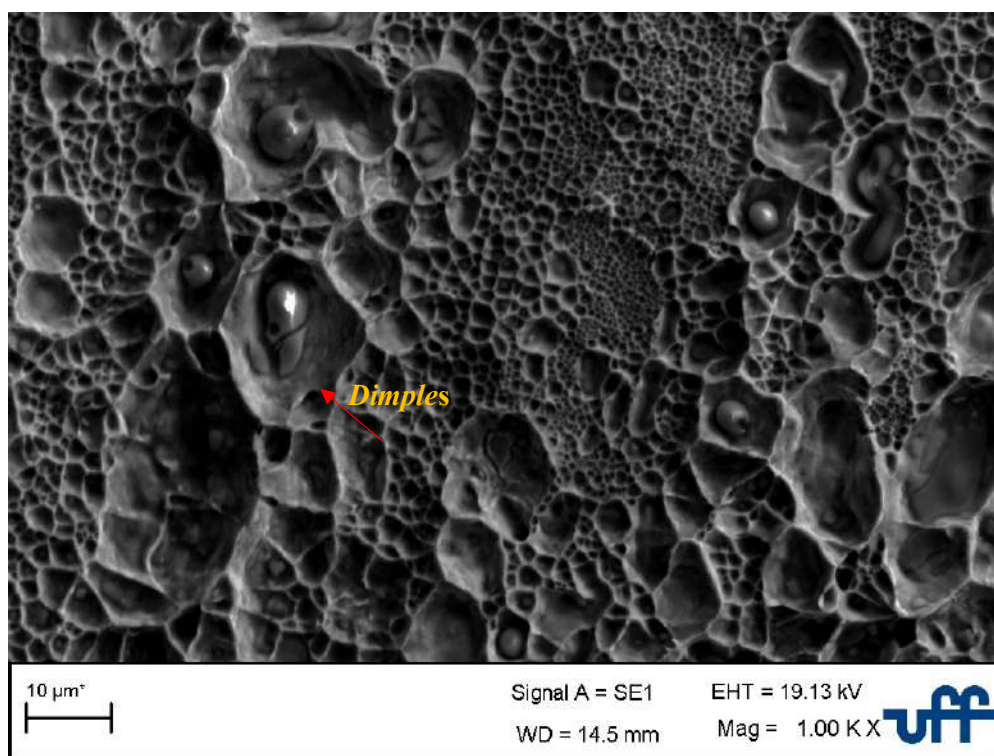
Fractografia da amostra S316LCR apresentando superfície de fratura dúctil.
